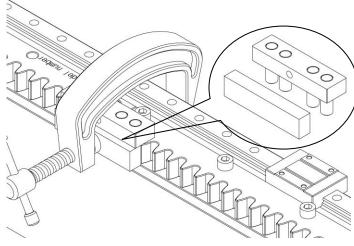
연결치구 고정방법 Figure 6. Clamping the alignment tool
